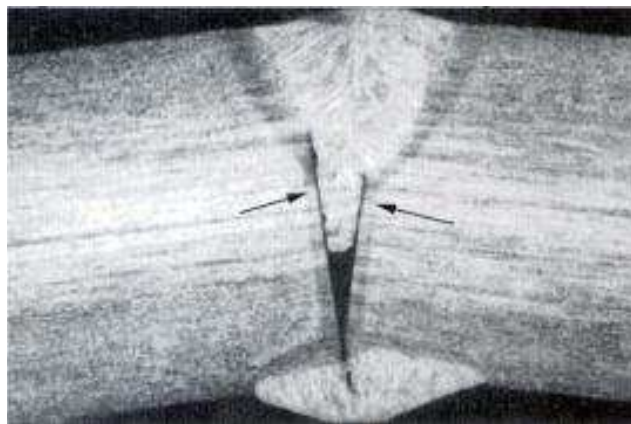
31 *Falta de fusión debido al ángulo de bisel de la junta soldada.
